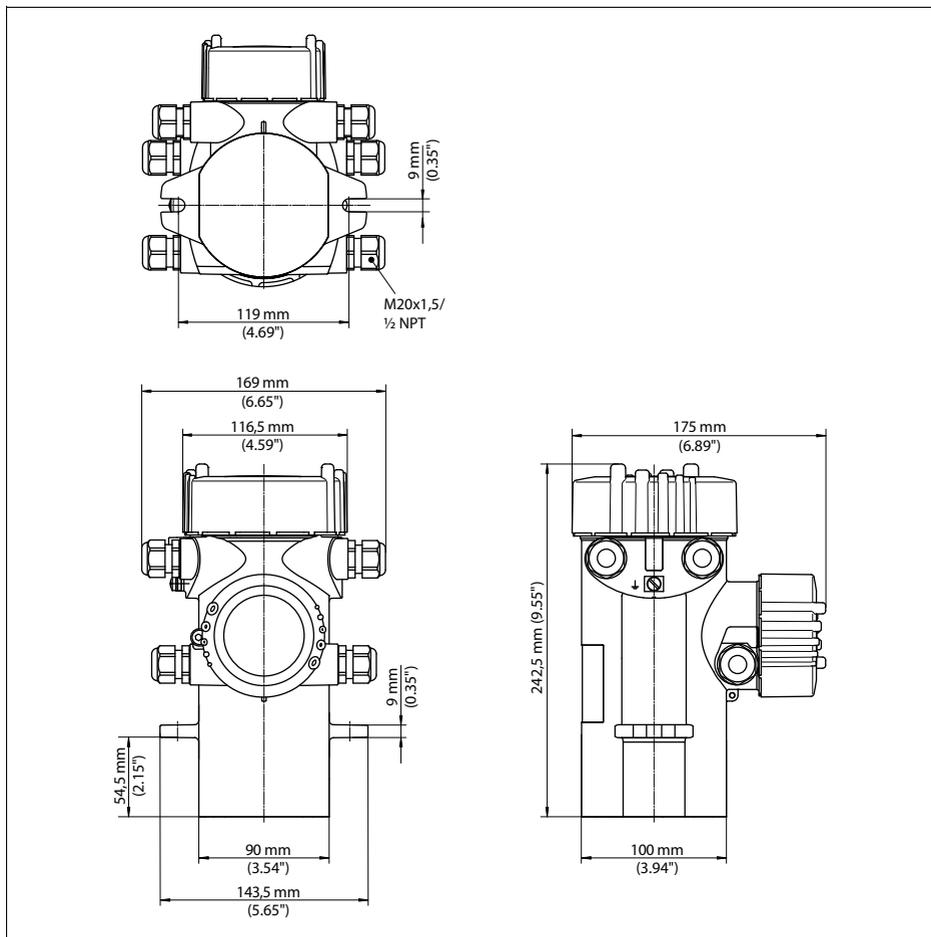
Корпус из алюминия или нержавеющей стали (точное литье)
